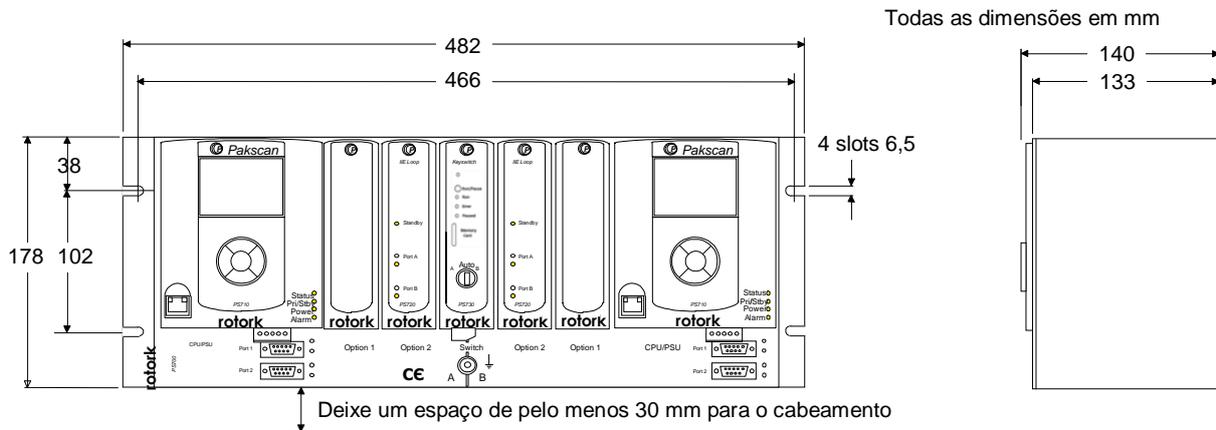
Pakscan 3, dimensões de montagem em rack de 19 polegadas.
